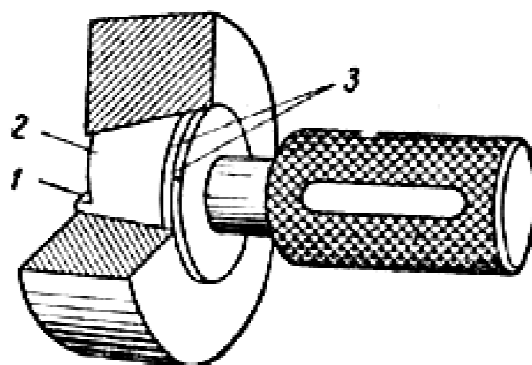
Проверка конического отверстия калибром-пробкой.
